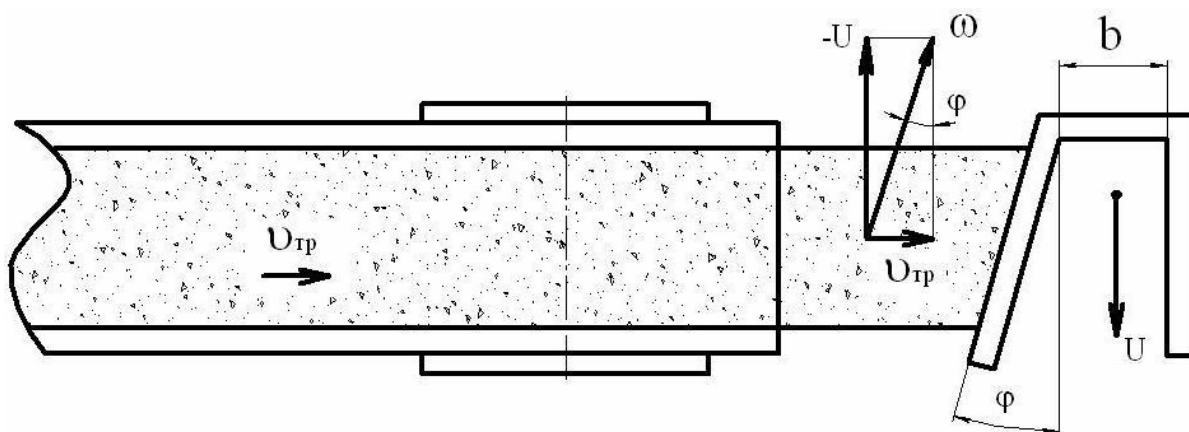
Схема подачи формовочной смеси на ротор пескомёта
